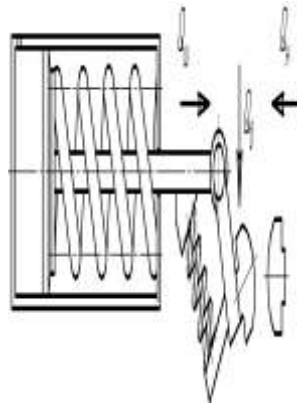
Кінематична схема електропневматичного контактора типу 1КП-005:
